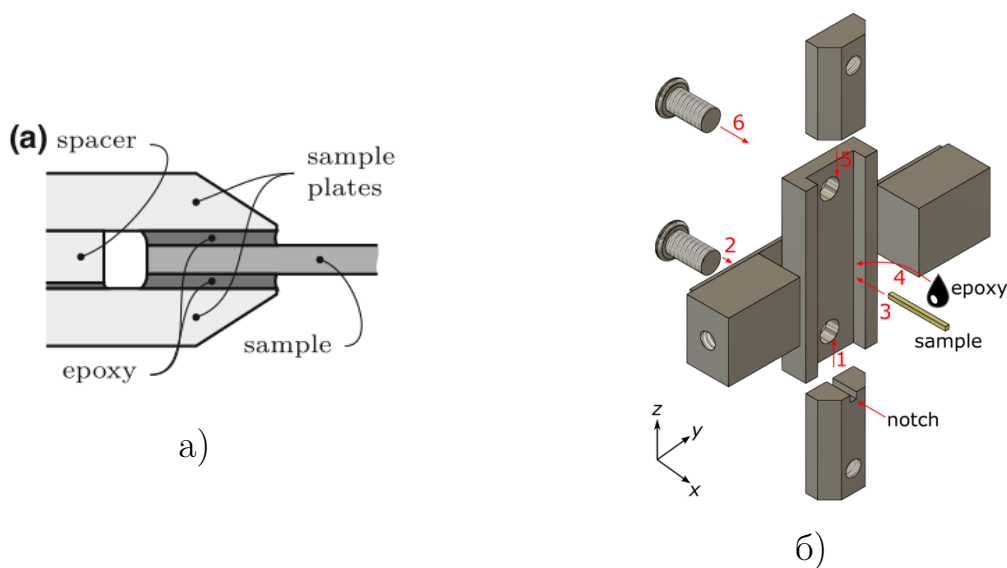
а) Крепление образца в работе [20]; б) Крепление образца в статье [21].
